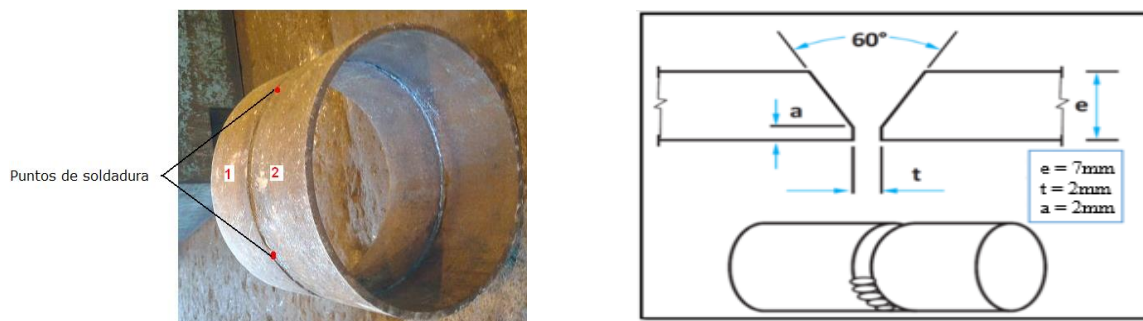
(a) Tubería para la soldadura. (b) Diseño de la junta.
